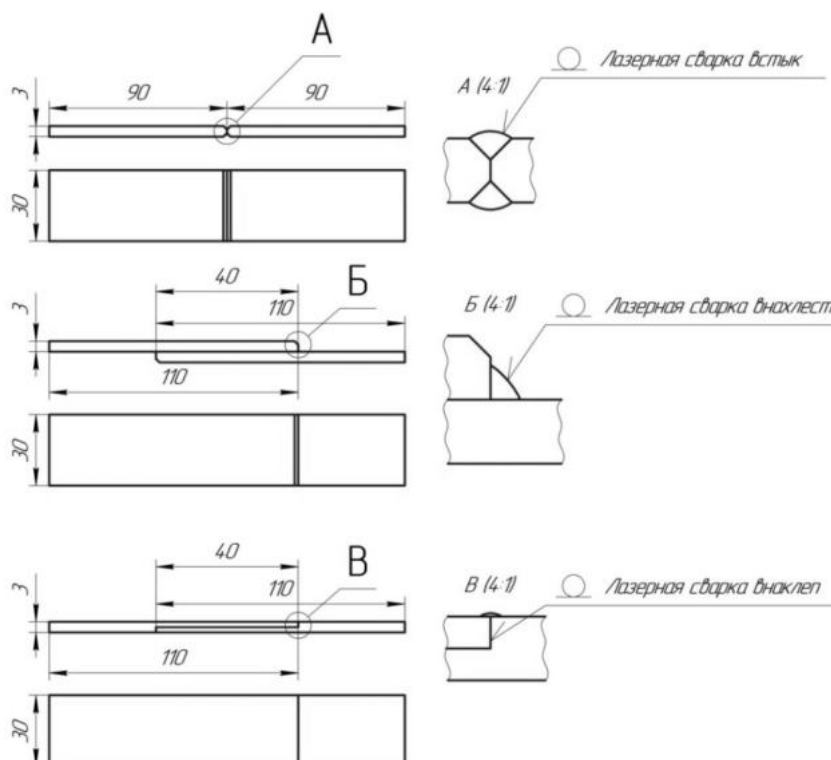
Схема образцов для сварки встык, внахлест, внаклеп
